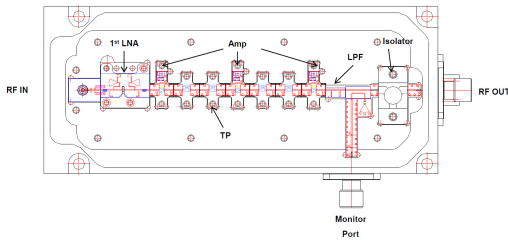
저잡음증폭장치의 PCB 배치 구조
